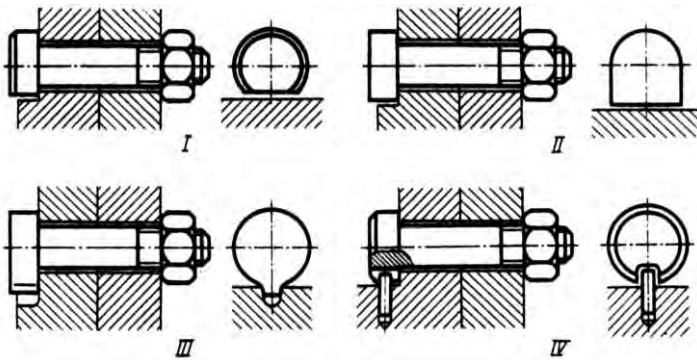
Ошибочные конструкции элементов, фиксирующих болт от проворота
